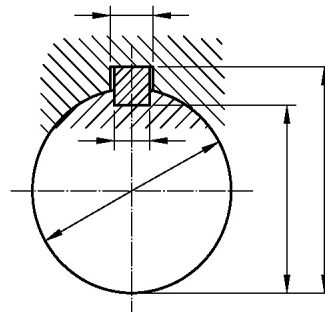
Acotación de conjuntos (eje + pieza + chaveta).
